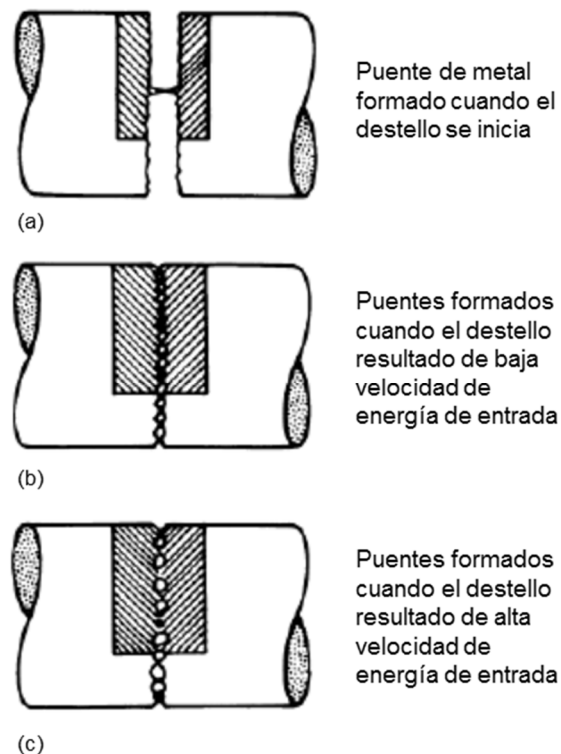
Incremento de los puntos de contacto producidos por la entrada de calor durante la soldadura por destello. (ASM, Flash Welding, 1993)
